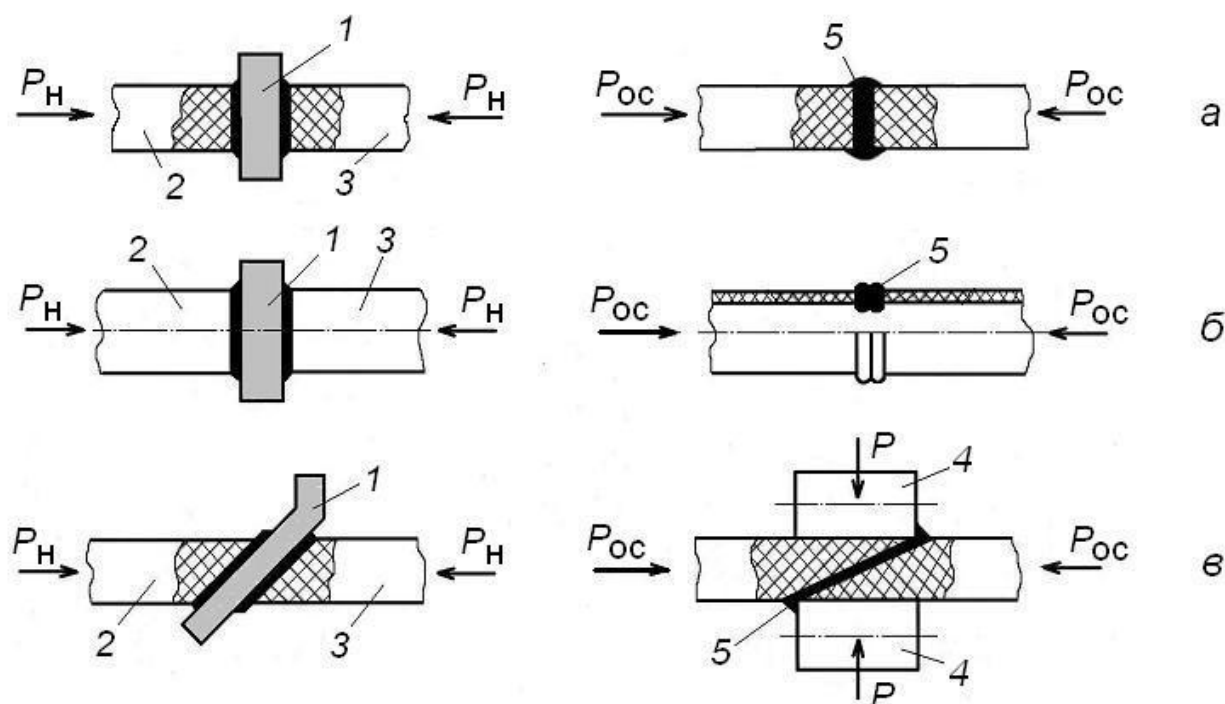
Схеми зварювання прямим нагріванням нагрітим інструментом: а - зварювання стрижнів встик; б - зварювання труб встик; в – зварювання з'єднання «на вус»: 1 – нагрітий інструмент; 2, 3 - зварювальні деталі; 4 – притискні ролики; 5 – зварний шов; ліворуч – нагрівання; справа – усадка; P_H - тиск при нагріванні; P_{OC} - тиск при усадці.
